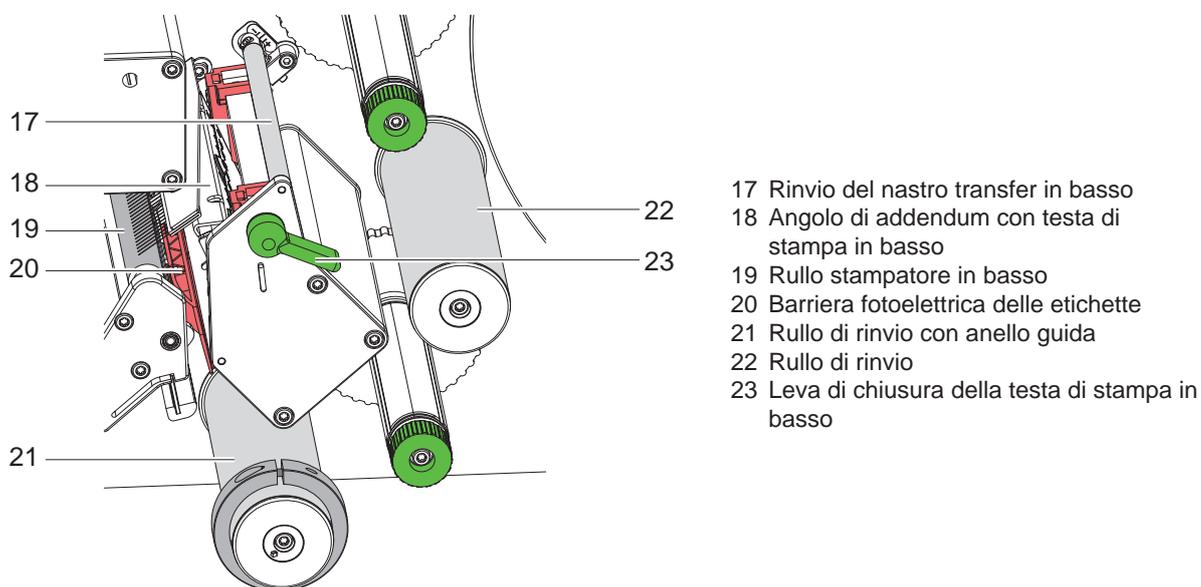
Meccanica di stampa – gruppo stampante inferiore per la stampa del colore complementare
